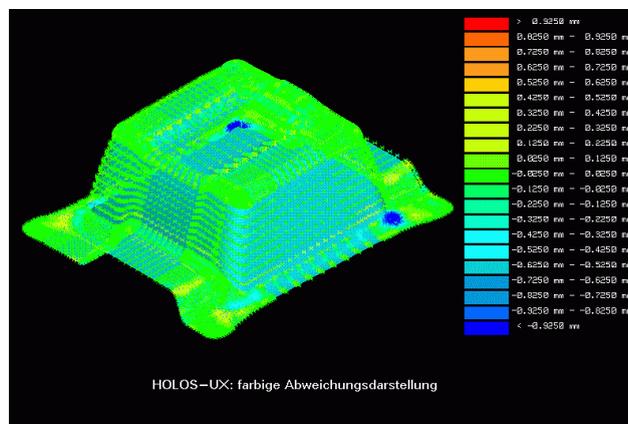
Resultados de medição de uma superfície com formas livres (Zeiss HOLOS-UX)
